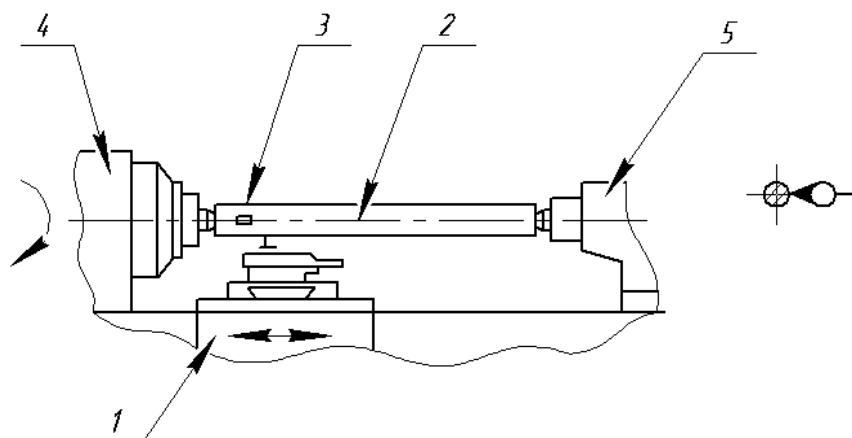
Схема проверки точности направляющих станины станка
